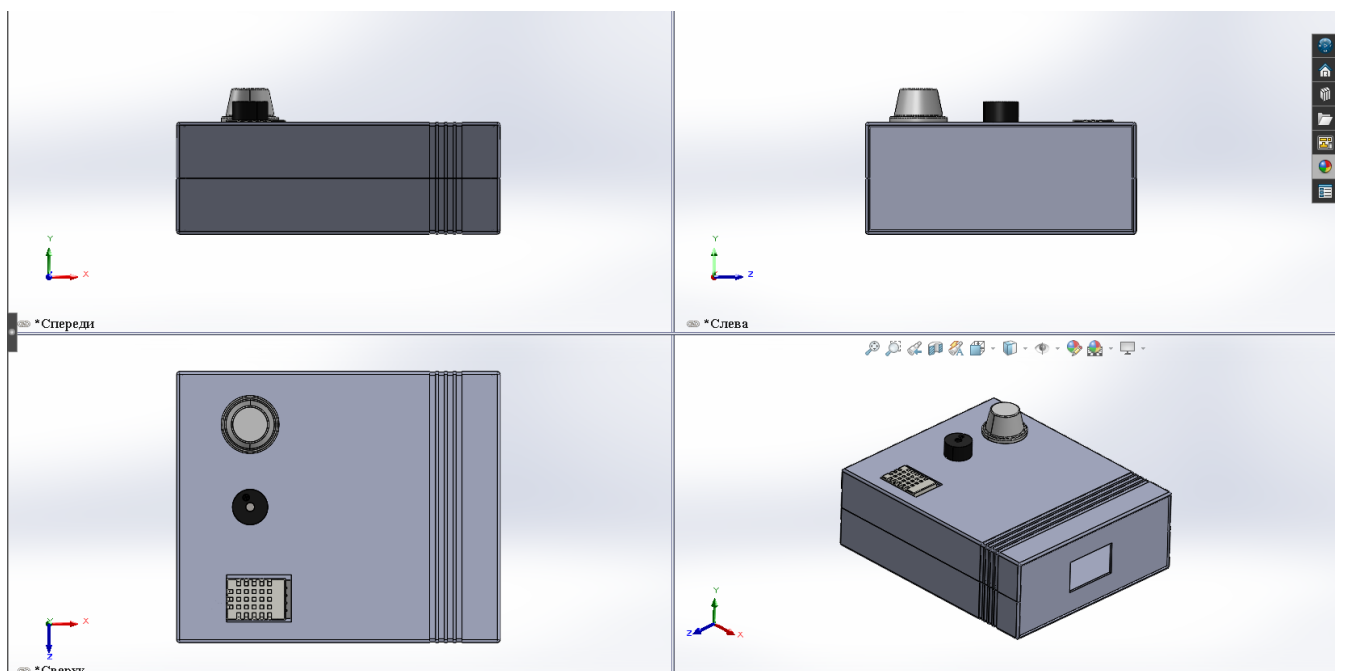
Тривимірна модель корпусу з установленими компонентами
